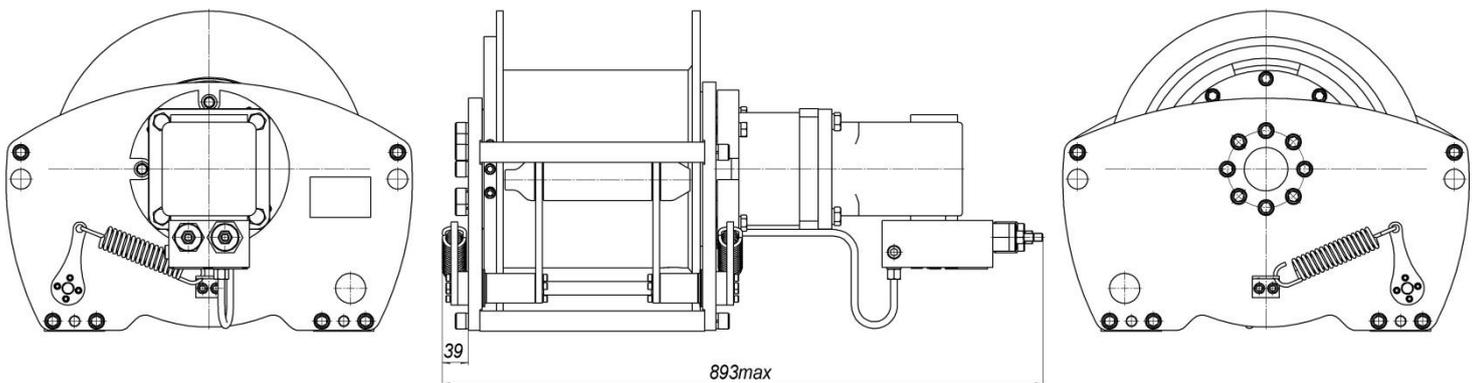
Общий вид, габаритные и присоединительные размеры
